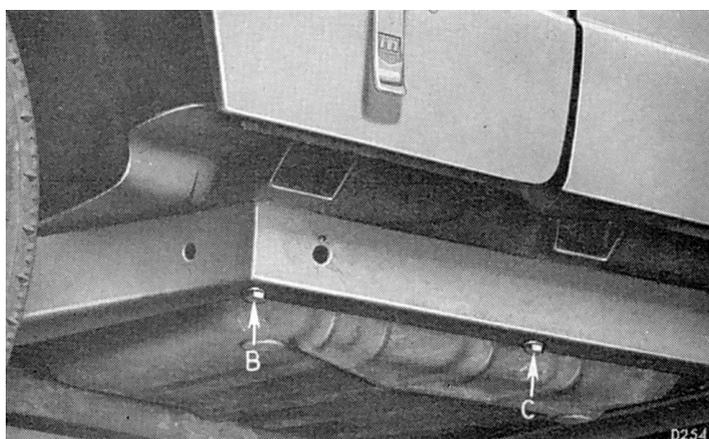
Boulon de fixation du plancher à la section latérale du châssis
